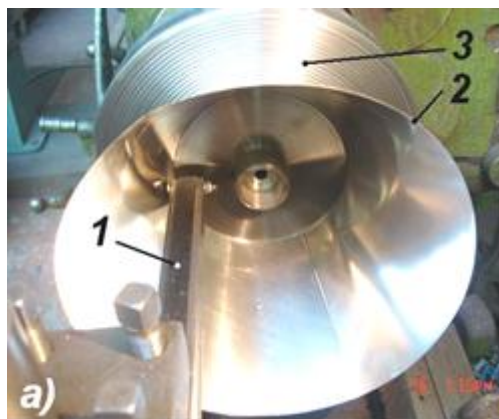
Процес виготовлення гофрованого диска; 1 - ротаційний пуансон; 2 - гладка конічна заготовка; 3 - форма-матриця з концентричними опорними ребрами
